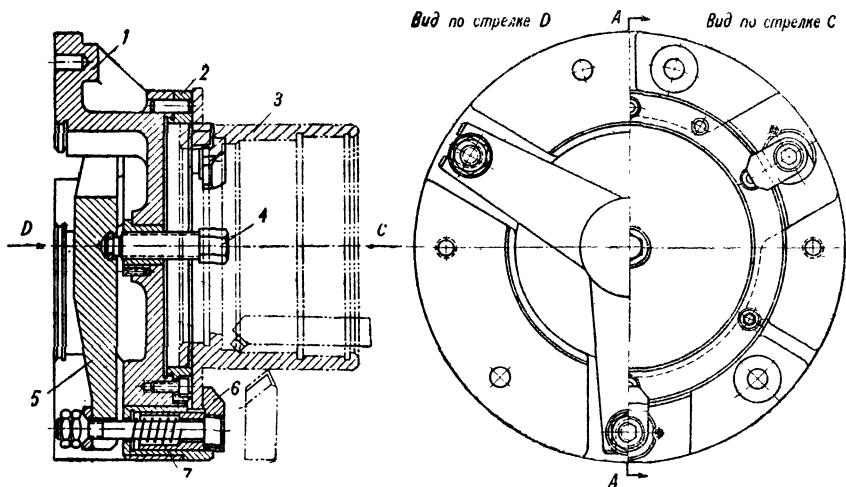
Рычажный патрон для крупных изделий с фланцем.
